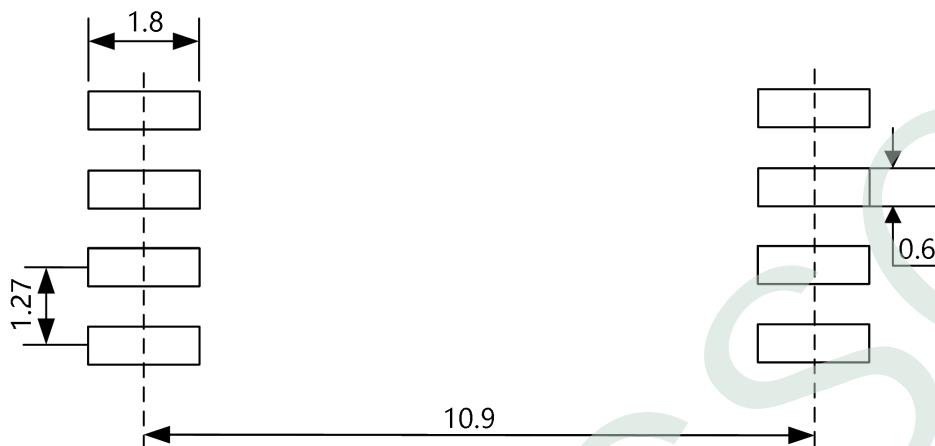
PCB 焊盘: 8-引脚 SOW
